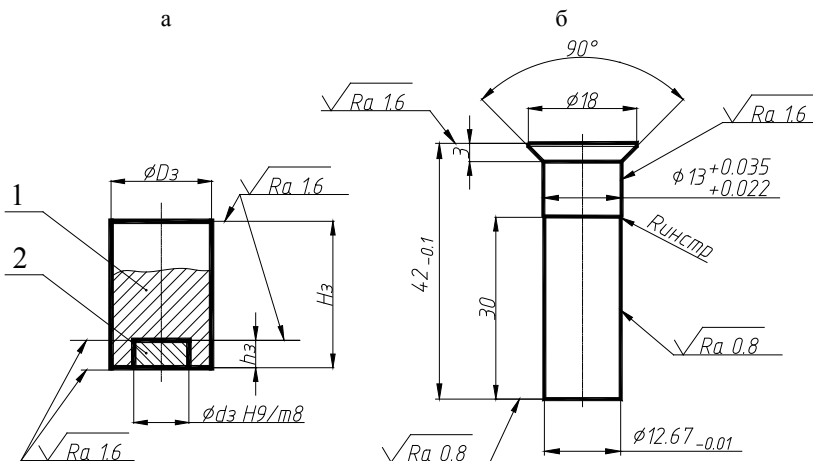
Эскизы: а – расчетной заготовки; б – готовой детали № 1039-4081-010.07/02 (в соответствии с номенклатурой инструментального производства РУП «Станкостроительный завод им. Кирова»): 1 – заготовка из основного материала (сталь 45, 40Х); 2 – плакирующий слой (сталь 5ХНМ, 5ХЗВЗМФС, 9ХС)
